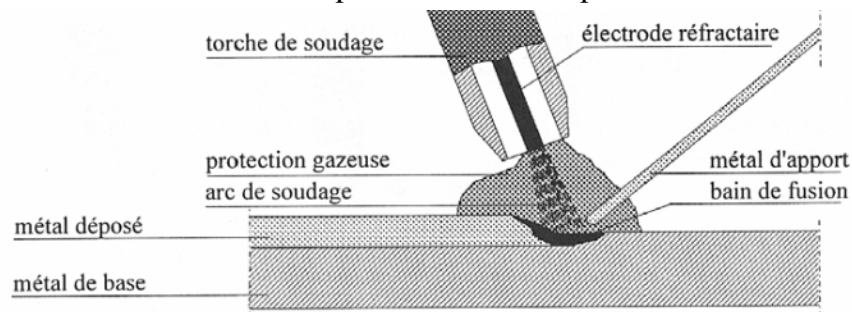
Soudage sous flux gazeux – Procédé TIG
